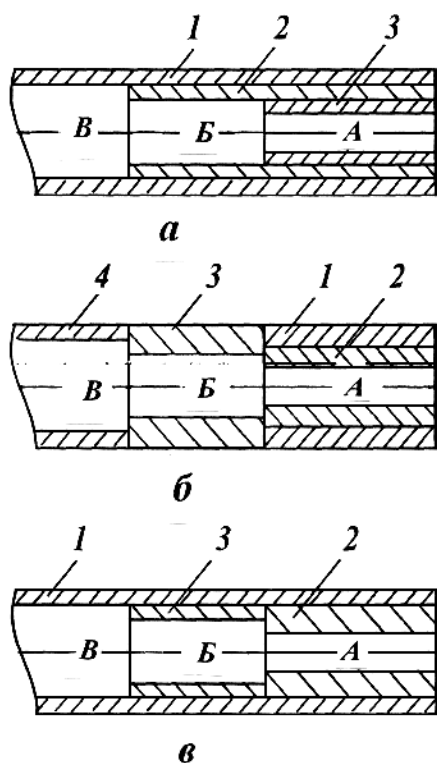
Схемы обтачивания ступеньчатого вала: 1...4 - номера переходов; А, Б, В - ступени вала.
